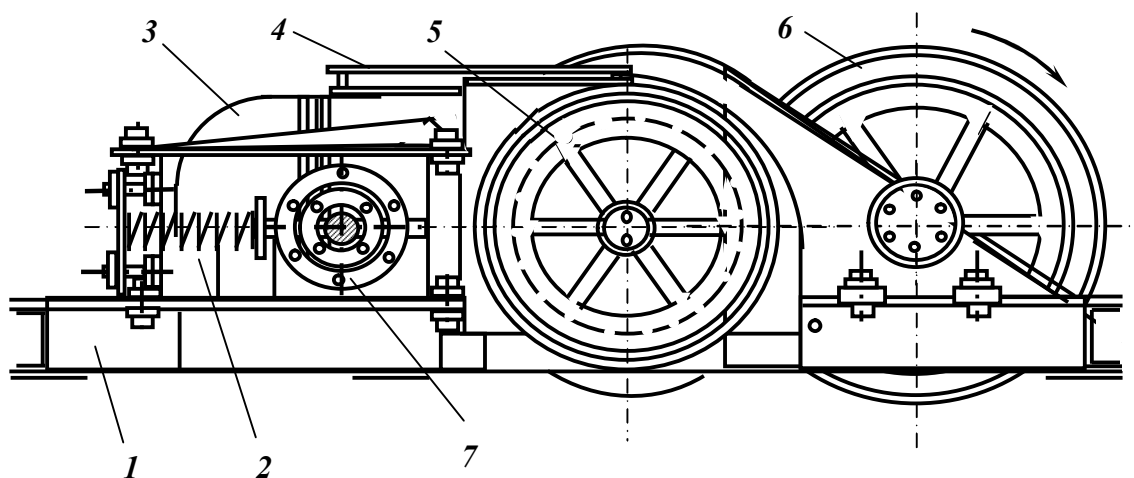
Двовалкова зубчаста дробарка типу ДДЗ.
